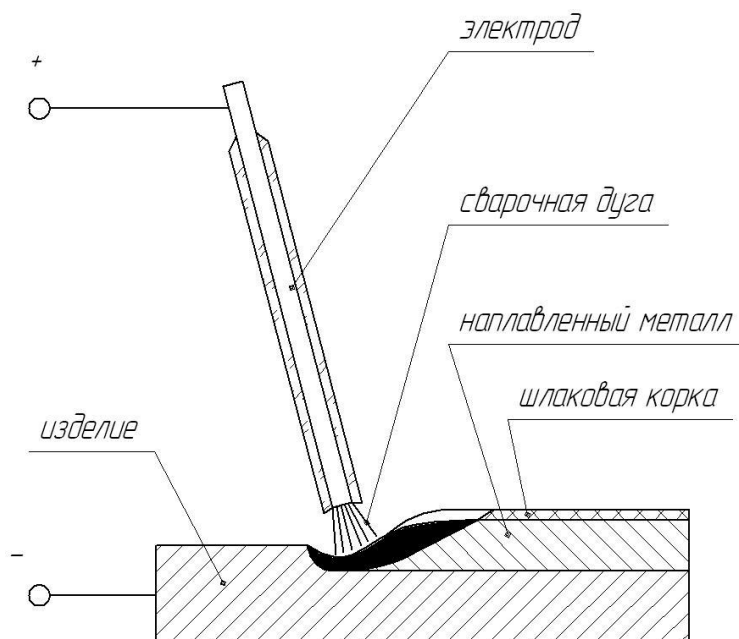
Схема выполнения ручной дуговой наплавки штучными электродами
